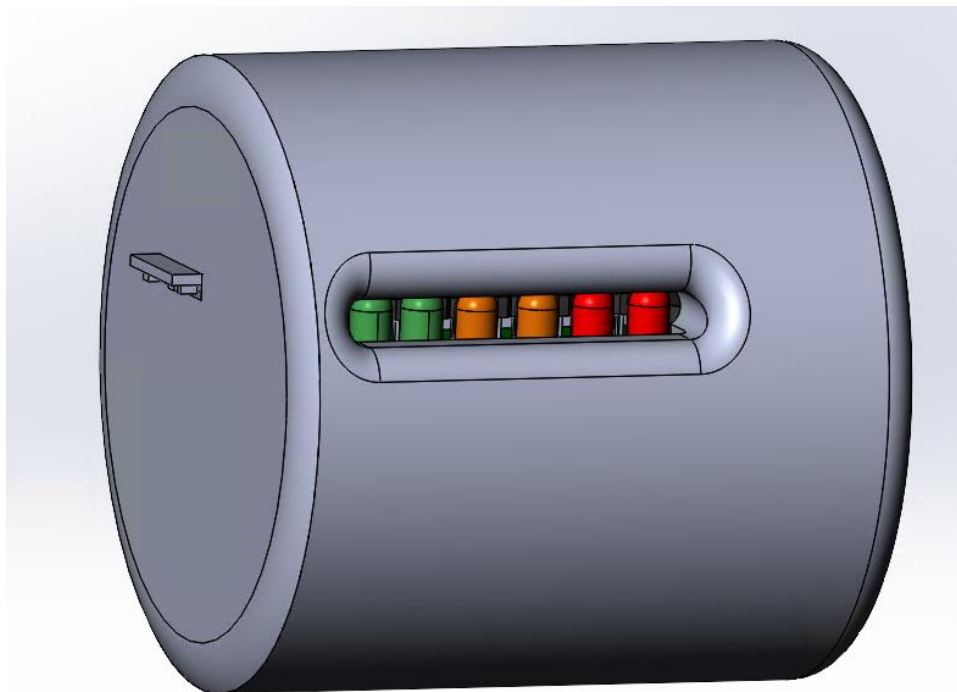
Загальний вигляд зібраного корпусу пристрою
